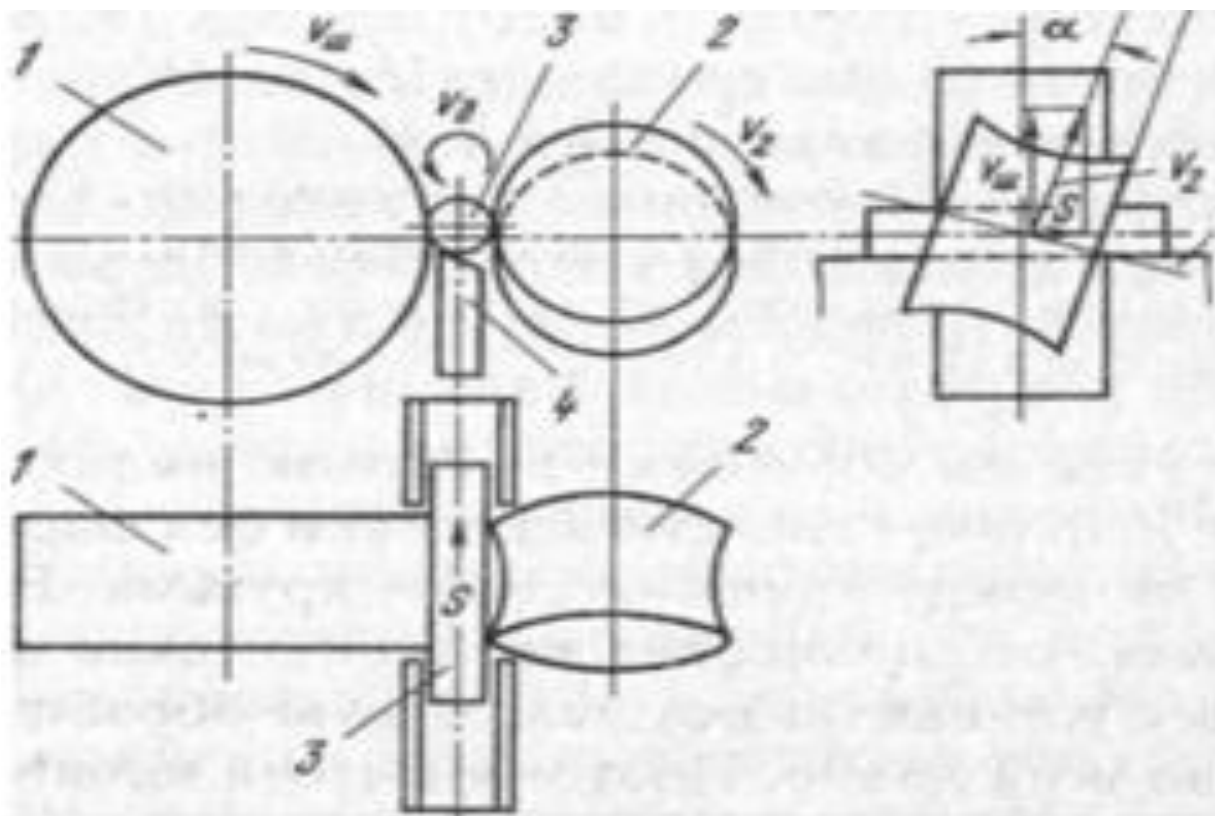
Схемы работы бесцентрового круглошлифовального станка: 1 – шлифовальный круг, 2 – ведущий круг, 3 – заготовка, 4 – опорный нож, $V_{ш}$ - окружная скорость шлифовального круга, $V_{з}$ – окружная скорость заготовки, V_2 – окружная скорость ведущего круга, α – угол поворота ведущего круга или наклона опорного ножа, S – продольная подача заготовки.
